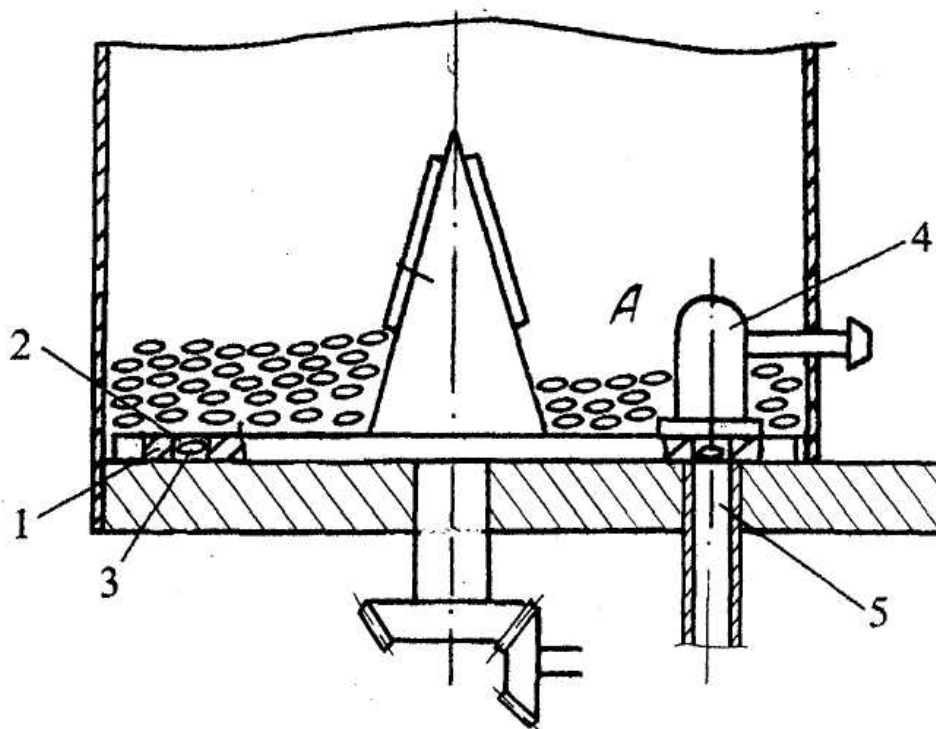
Принципова схема дискового пневмомеханічного апарата.
